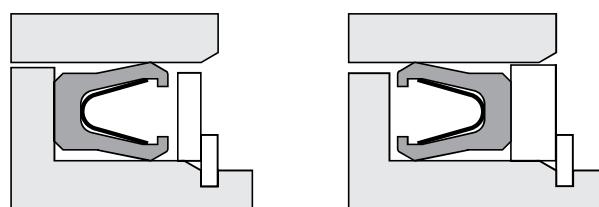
Посадочная канавка с фиксатором упорного кольца: установка «задней кромкой вперед» и «губками вперед»
